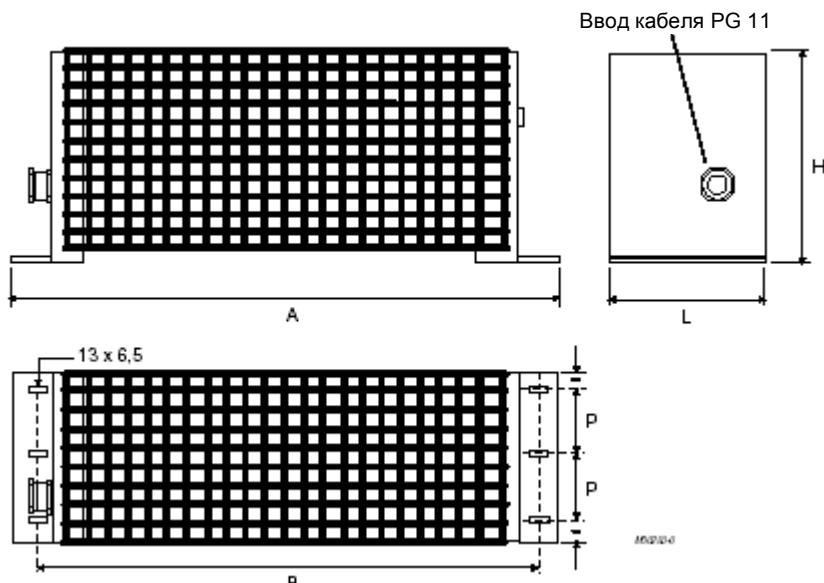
Размеры тормозных резисторов 4кВт, 8кВт и 12кВт
